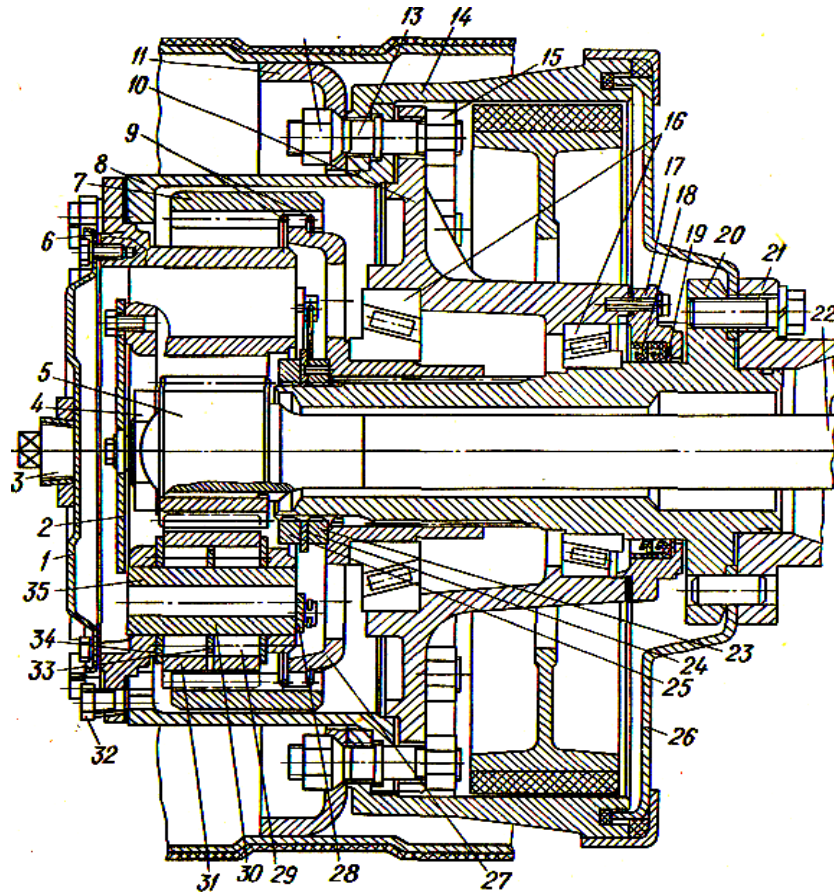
Бортовий редуктор ведучого моста трактора ХТЗ-181:
